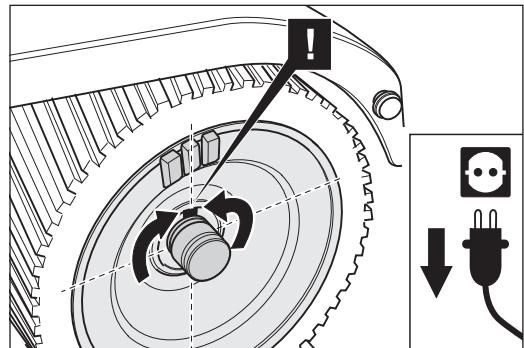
Die Schleifwalze so weit drehen, bis die Passfedernut nach oben zeigt. So kann die Passfeder nicht aus der Welle fallen.
